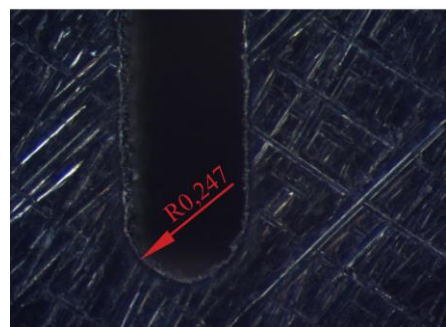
Образцы для испытаний на ударный изгиб
